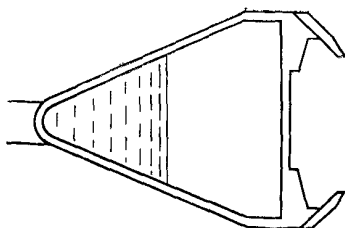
Поперечное сечение сварной станины плоскошлифовального станка фирмы Snow
